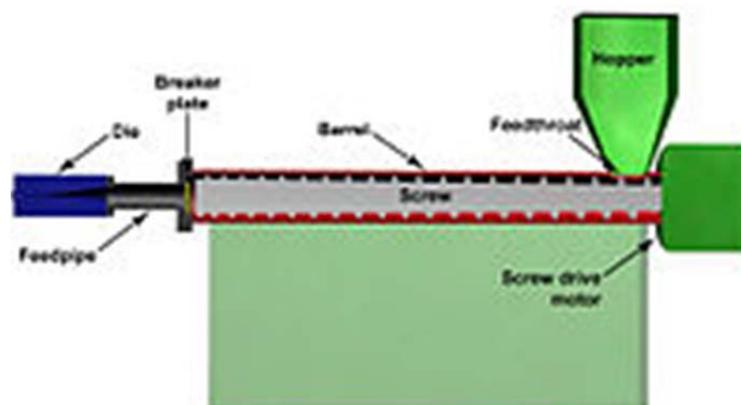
Vista en sección de la extrusión de plásticos, mostrando los componentes.
